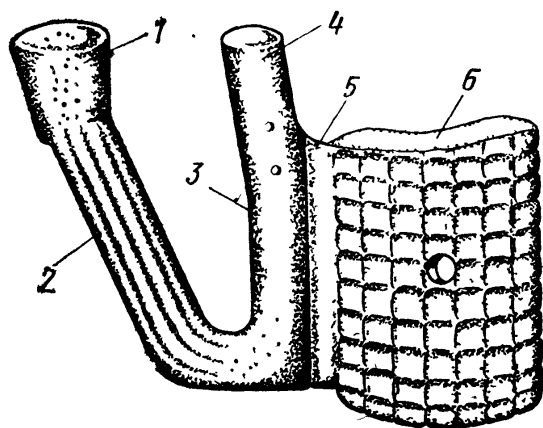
Отливка поршня с улучшенной конструкцией литниковой системы [53]:
